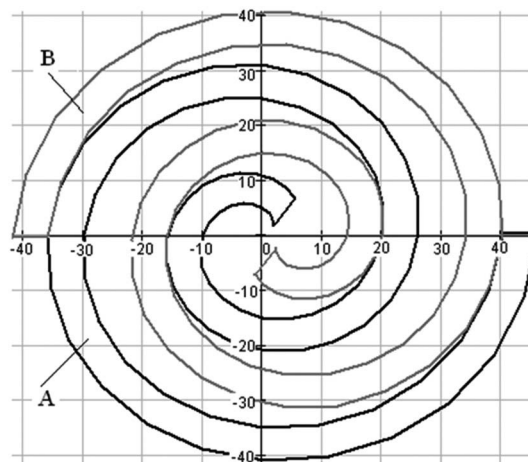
Профильный расчет образующих спиралей холодильного компрессора
